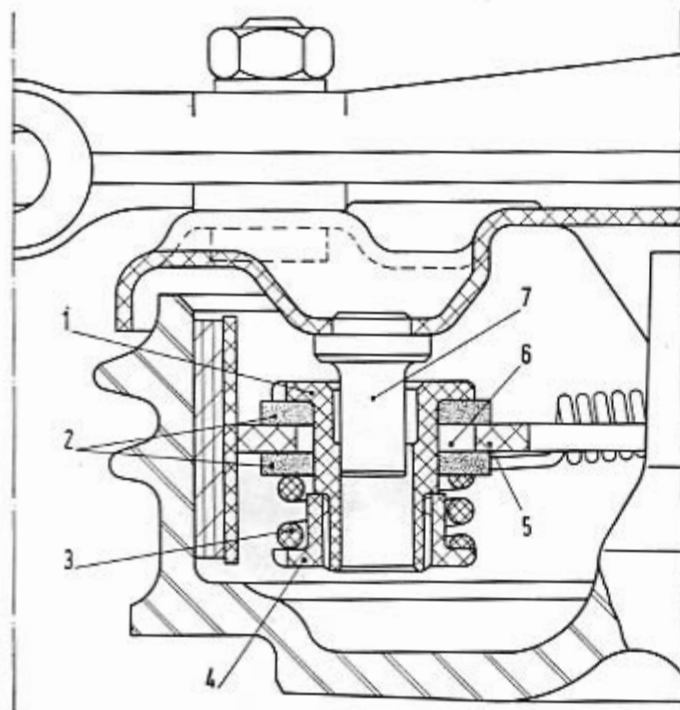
Coupe d'un dispositif auto-régleur pour le rattrapage du jeu entre mâchoires et tambour.
